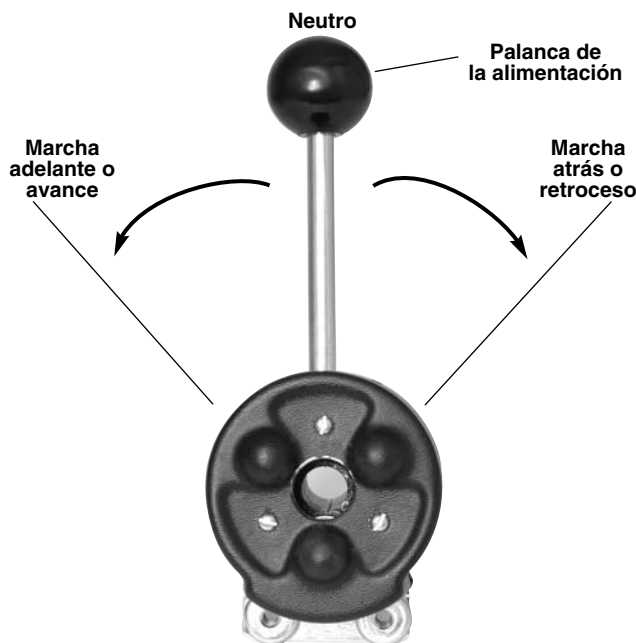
Palanca de cambios del AUTOFEED (visto desde la parte delantera de la máquina)
